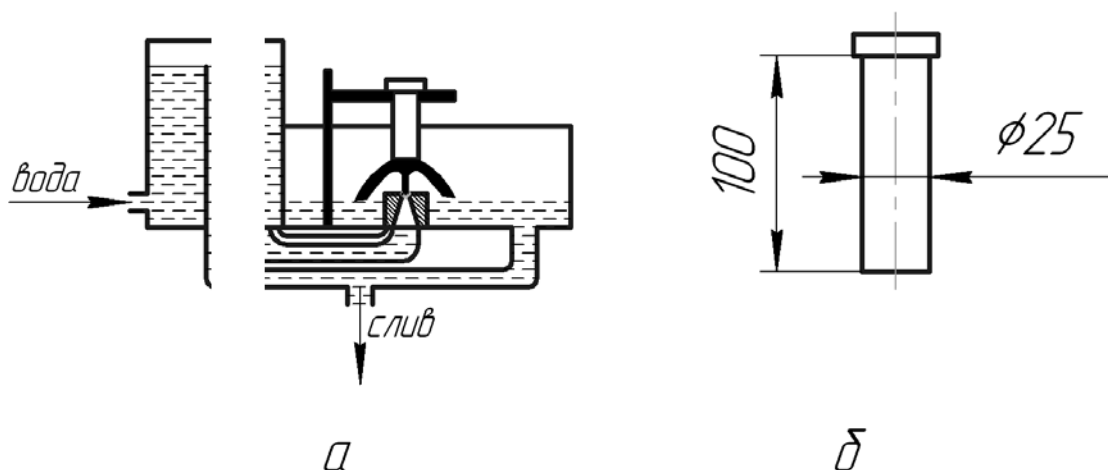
Установка (а) и образец (б) для торцевой закалки
